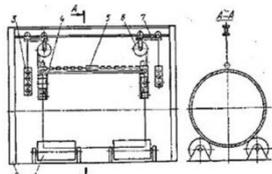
Слайд 2 «Установка для сборки продольного стыка обечайки»
